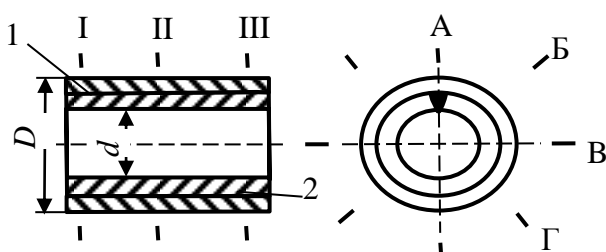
Схема измерения образцов: 1 – обойма; 2 – втулка из сварной трубы
